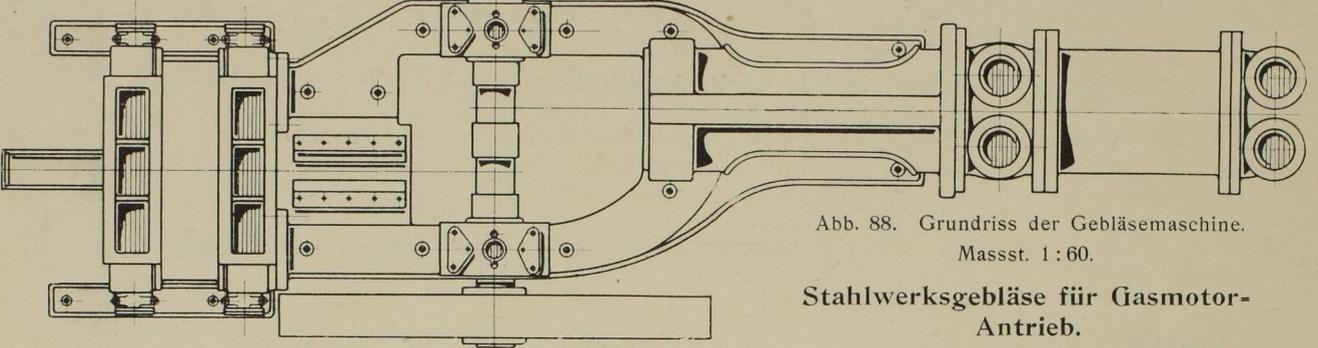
Grundriss der Gebläsemaschine.
